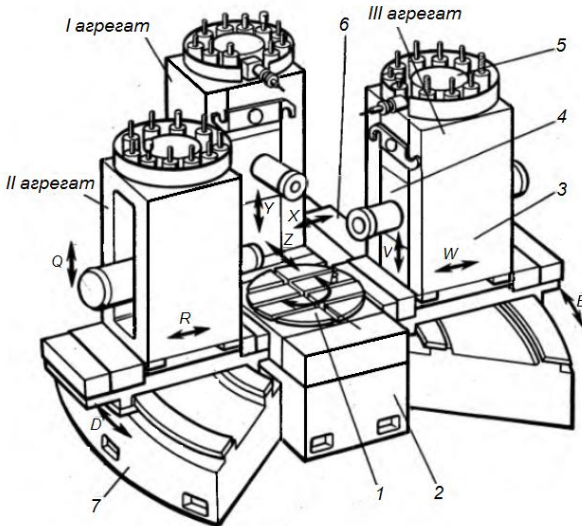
Компонування агрегатного верстата з ЧПК
